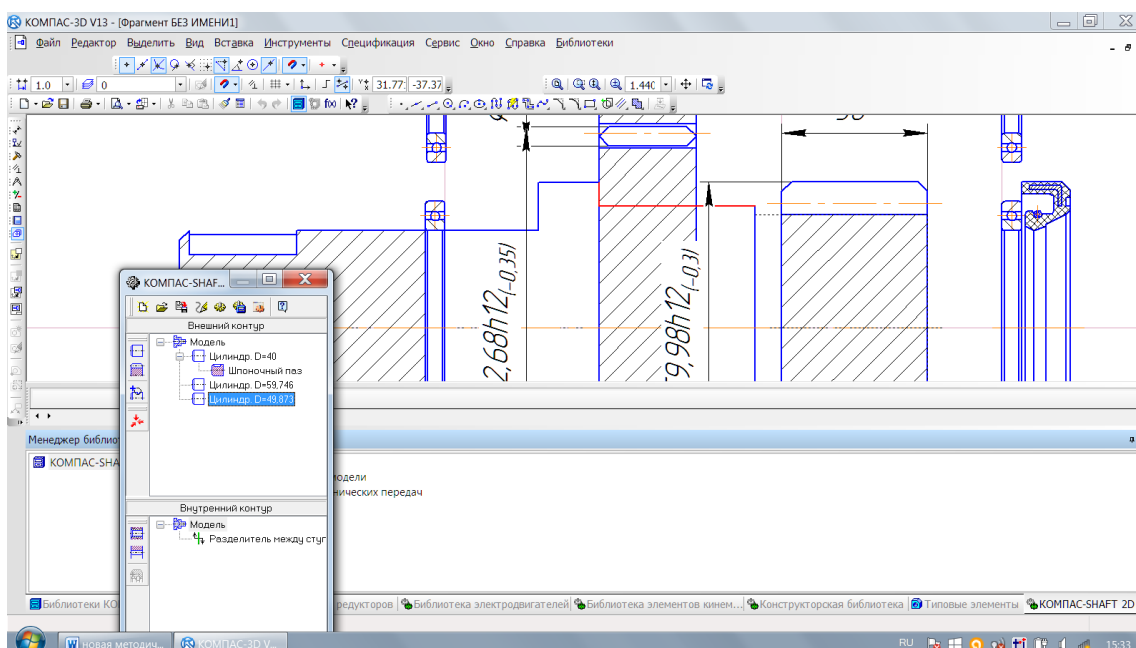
Построение заплечика вала на эскизной компоновке редуктора
